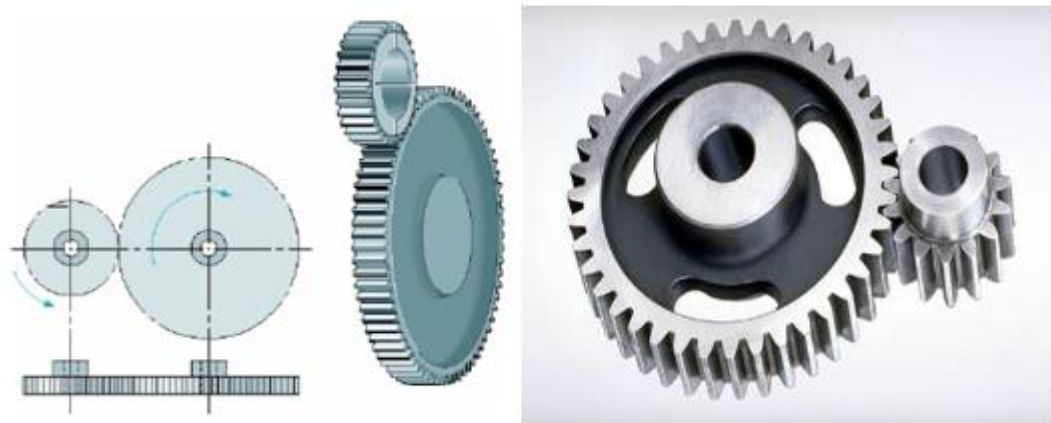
Engrenagens cilíndricas de dentes retos [14]
